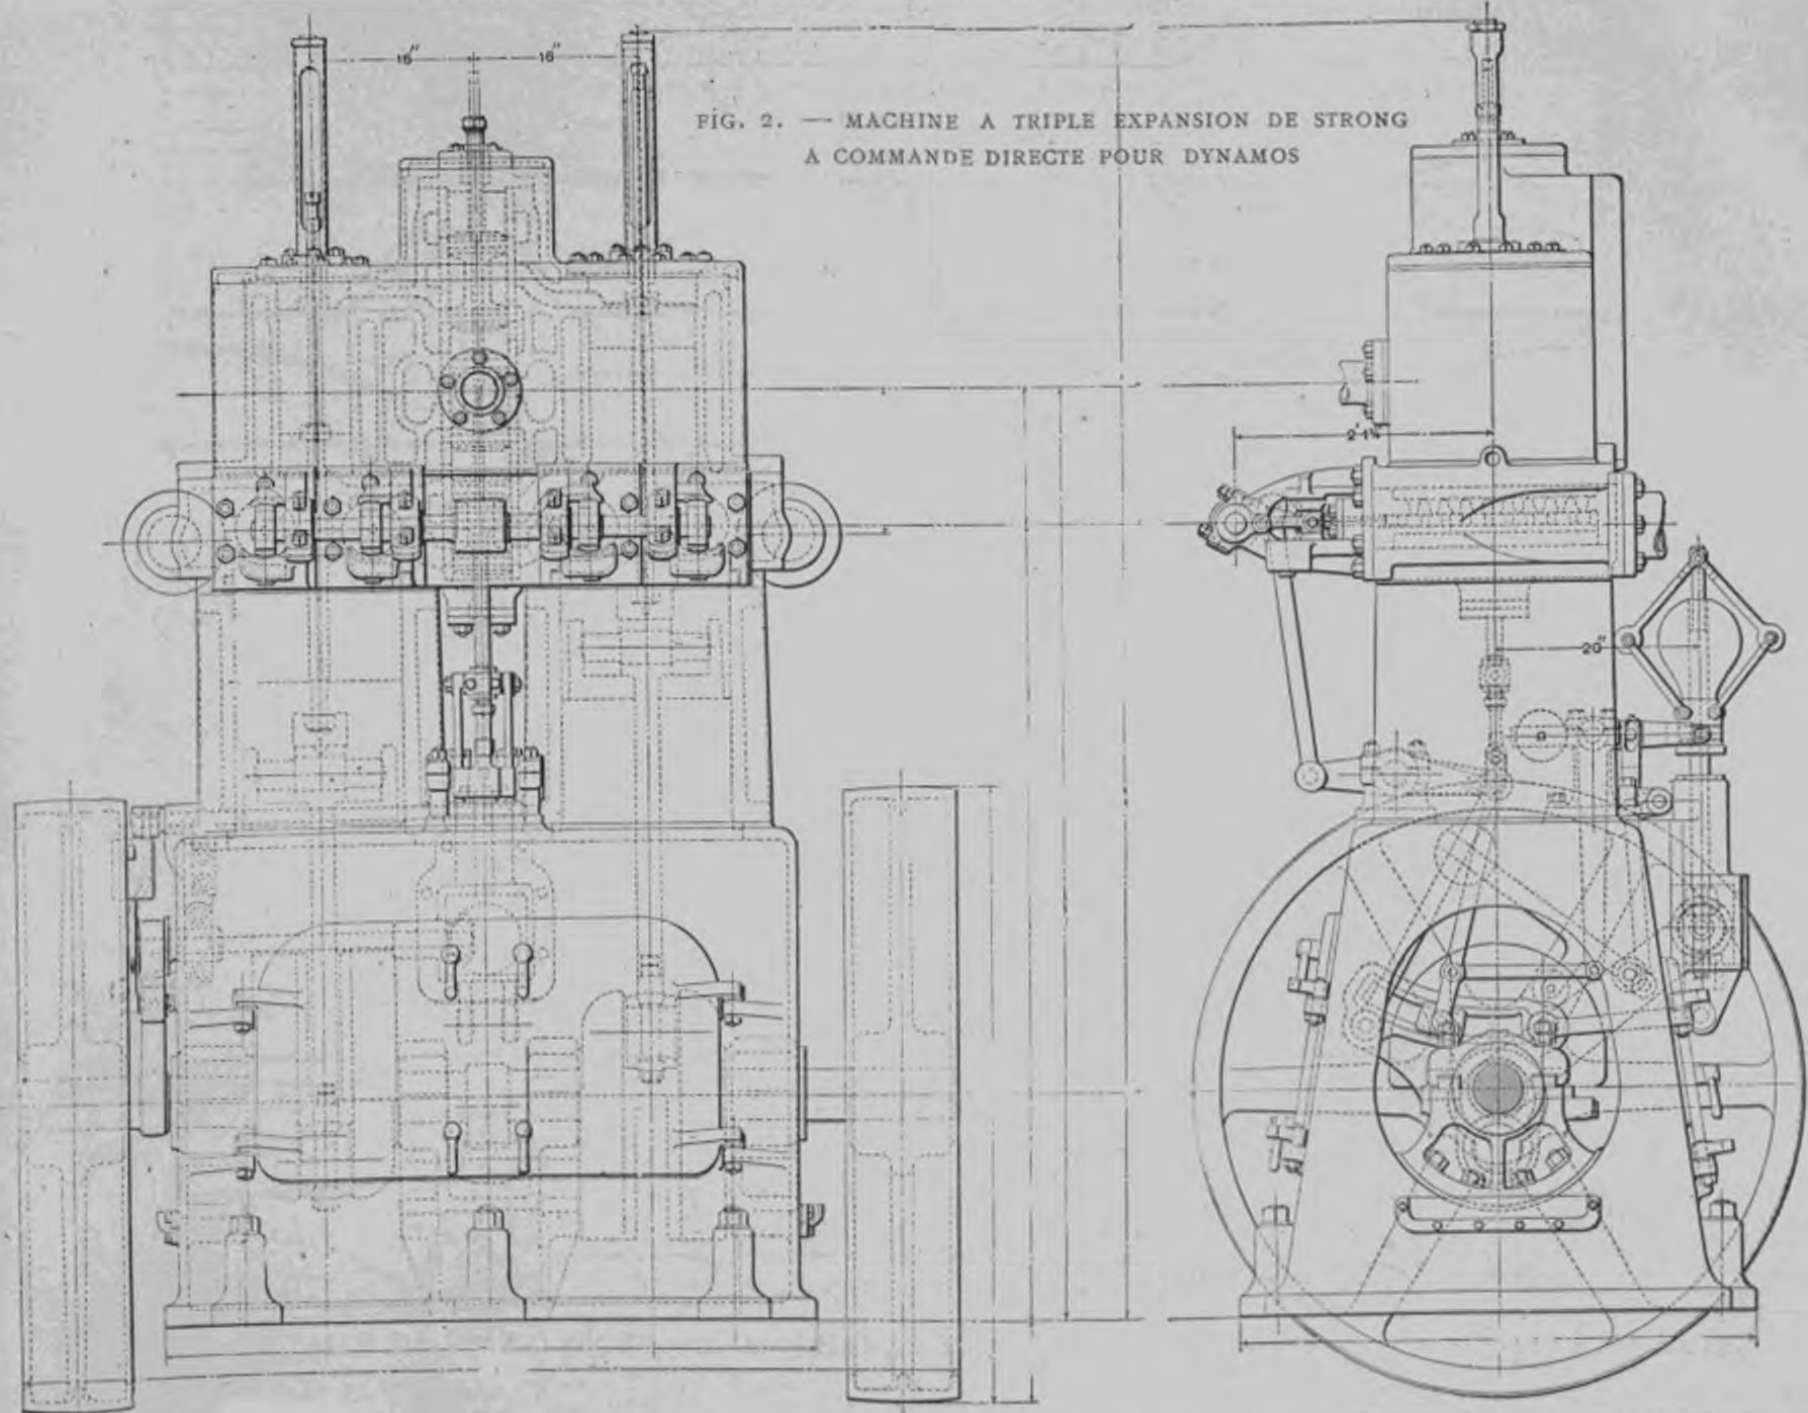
MACHINE A TRIPLE EXPANSION DE STRONG
